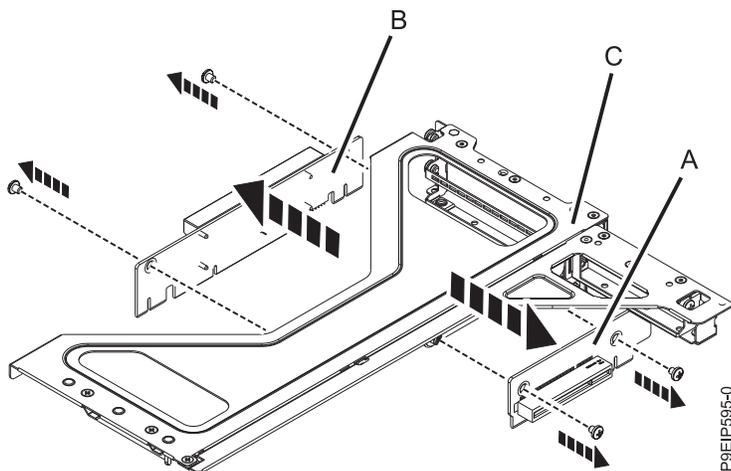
Extracción de las tarjetas de expansión PCIe de la caja del adaptador PCIe
